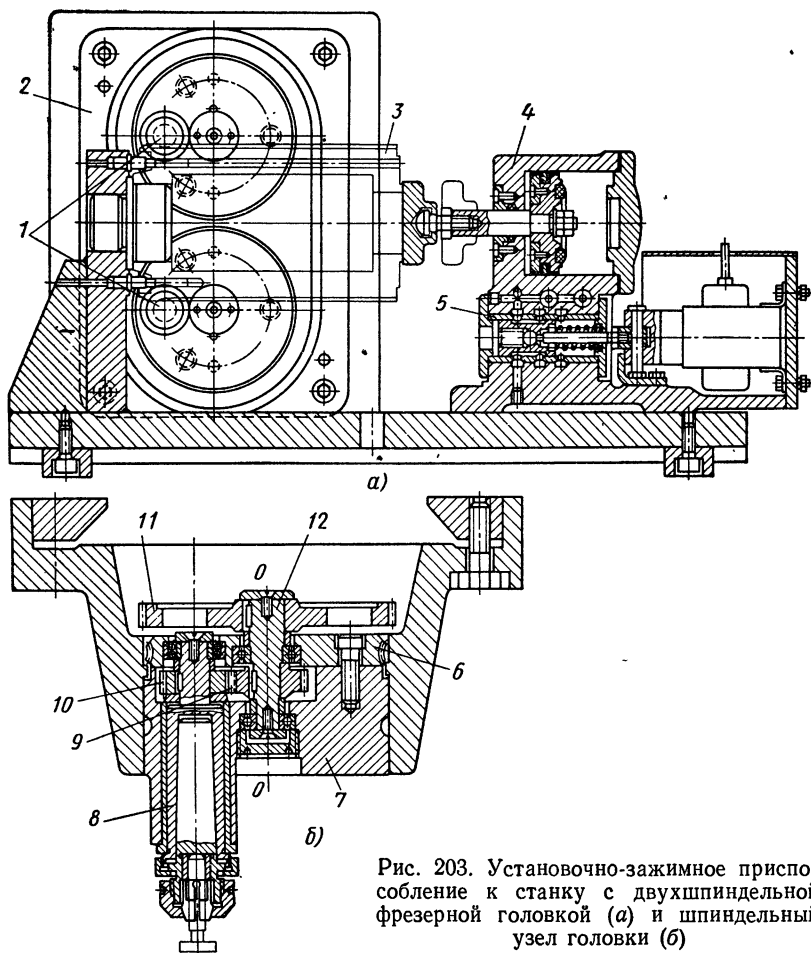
Установочно-зажимное приспособление к станку с двухшпиндельной фрезерной головкой (а) и шпиндельный узел головки (б)
